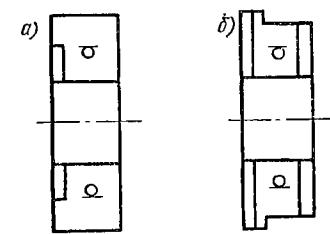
Условное изображение подшипника с указанием типа и конструктивных особенностей: а — радиальный шариковый однорядный с односторонним уплотнением; б — радиальный шариковый однорядный с двумя защитными шайбами
